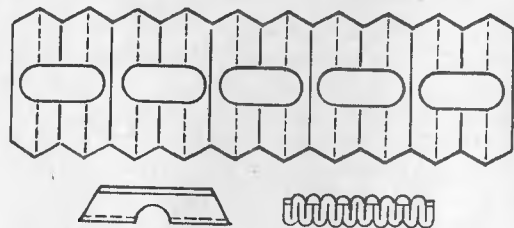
Магнитный пазовый клин, опрессованный пластмассой
